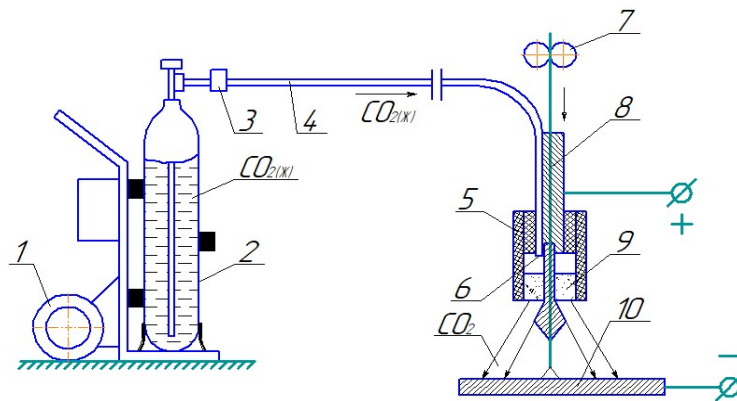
Принципиальная схема газопитания и охлаждения сварочной горелки жидкой  $\text{CO}_2$ : 1 — тележка; 2 — сифонный стальной баллон с  $\text{CO}_2$ ; 3 — индикатор с фильтром–отсекателем; 4 — шланг высокого давления; 5 — сварочная горелка; 6 — дроссель с калиброванным отверстием; 7 — ролики подачи электродной проволоки; 8 — токоподводящий мундштук с наконечником; 9 — газопроницаемый вкладыш; 10 — изделие [2]
